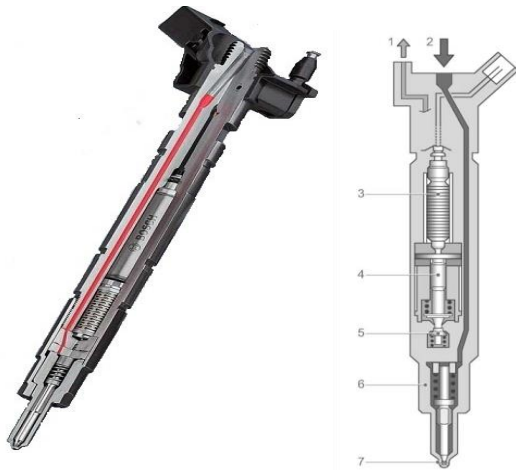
Конструкція форсунки з п'єзоелектричним приводом фірми Bosch: 1 - лінія зливу палива; 2 - лінія подачі палива; 3 - модуль п'єзоелектричного приводу; 4 - гідравлічний компенсатор; 5 - клапан керування; 6 - розпилювач; 7 – сопло
